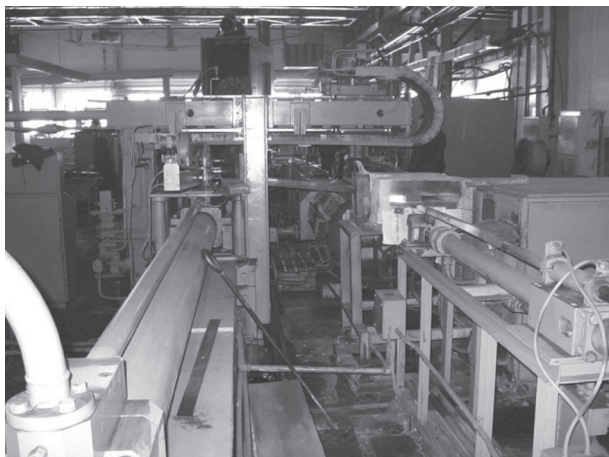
Внешний вид стана для прокатки заготовок направляющих опор пневмоподвески
